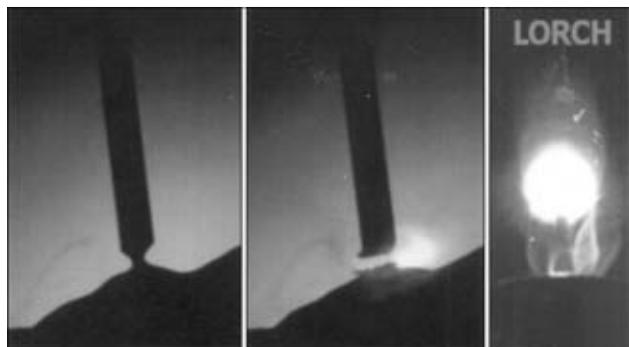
Детализация процесса сварки с режимом «Speed Root»
